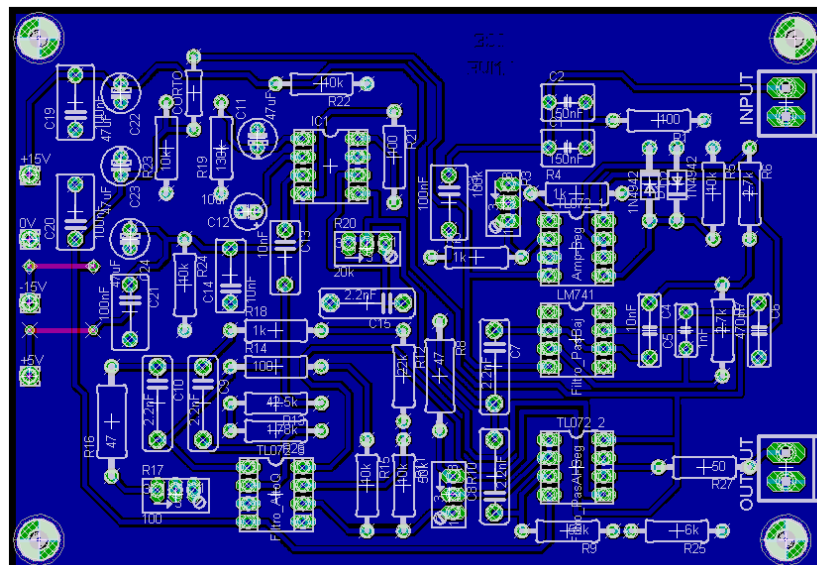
Vista del diseño del módulo depurador y acondicionador de señal en circuito impreso.
